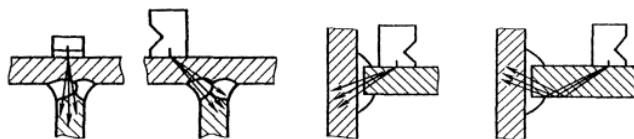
Схемы ультразвукового контроля качества тавровых сварных соединений
